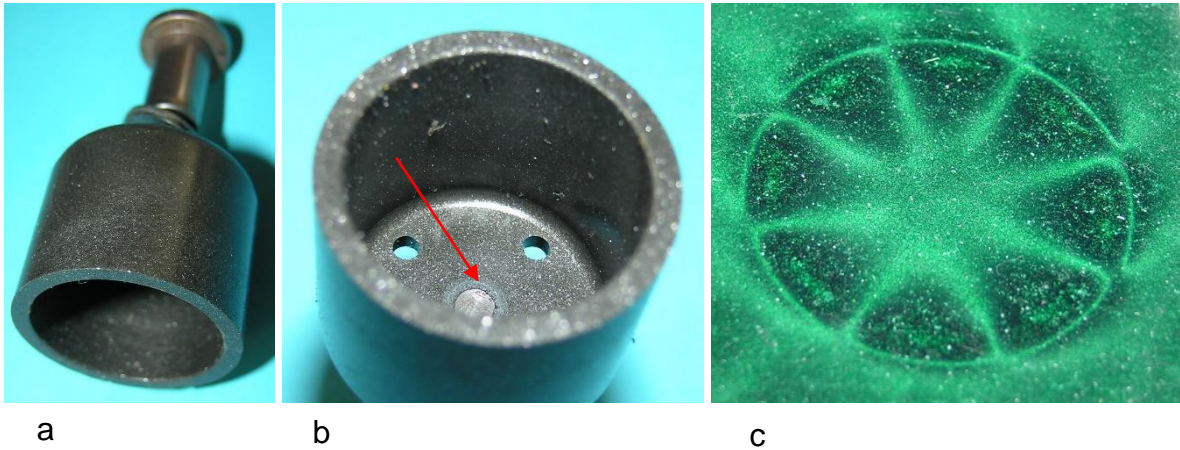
Glockenläufer: a) Magnetglocke mit Welle, b) Innenraum: Wandstärke 2 mm, Außendurchmesser 26 mm, Länge 22 mm, c) Achtpolige Magnetisierung
